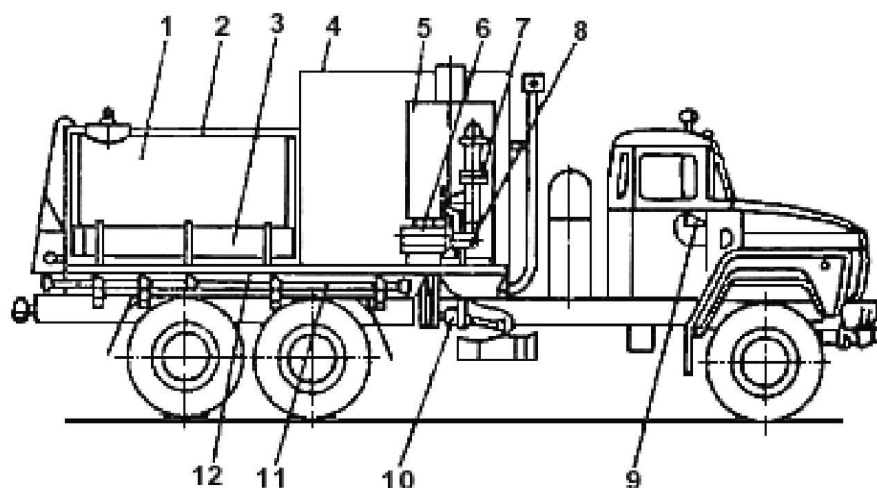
Промысловая паровая передвижная установка ППУА-1600/100:
